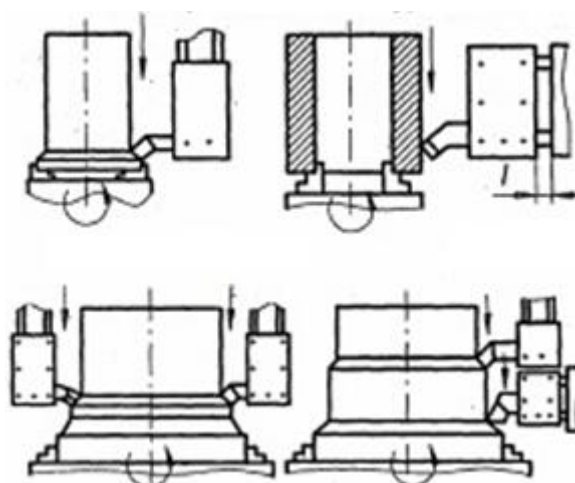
Схемы обработки на токарно-карусельных станках
